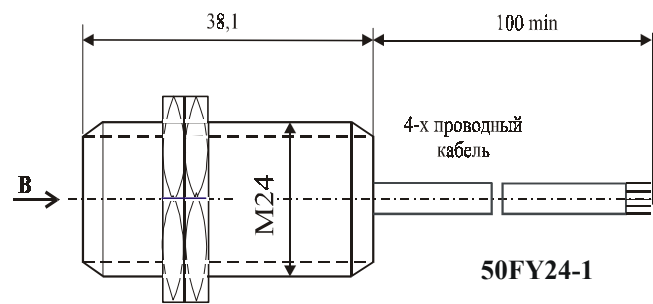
Внешний вид и габаритные размеры датчиков типа 50FY24
